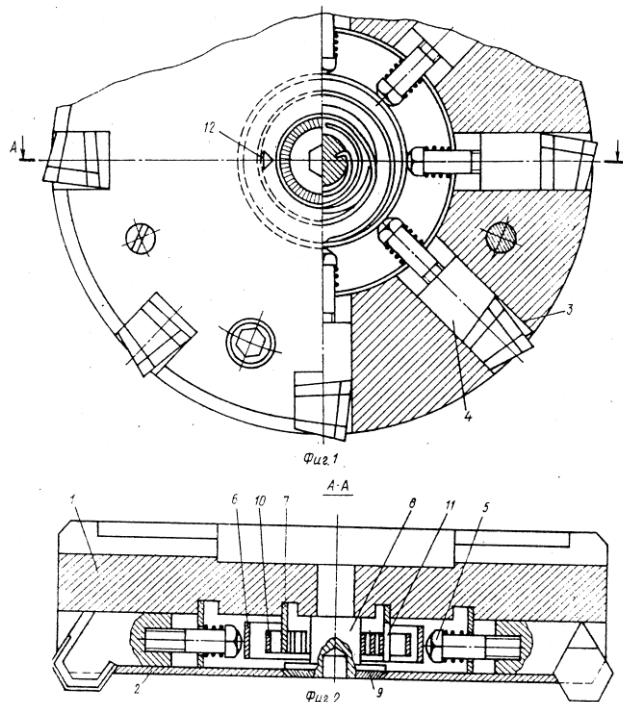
Торцева фреза по а. с. 806293 МКИ В 23 С 5/06
